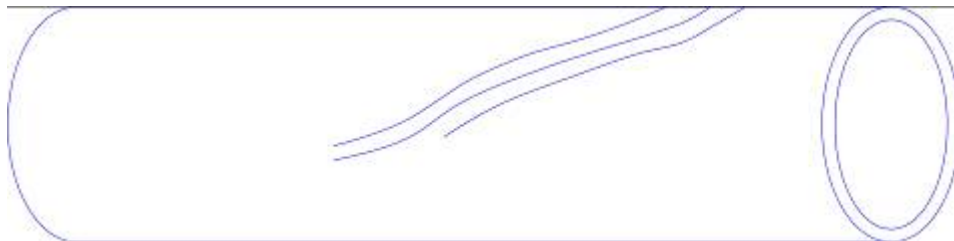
Прокатные плены группового расположения на наружной поверхности трубы, образующиеся при раскатывании морщин, имевшихся на заготовке
